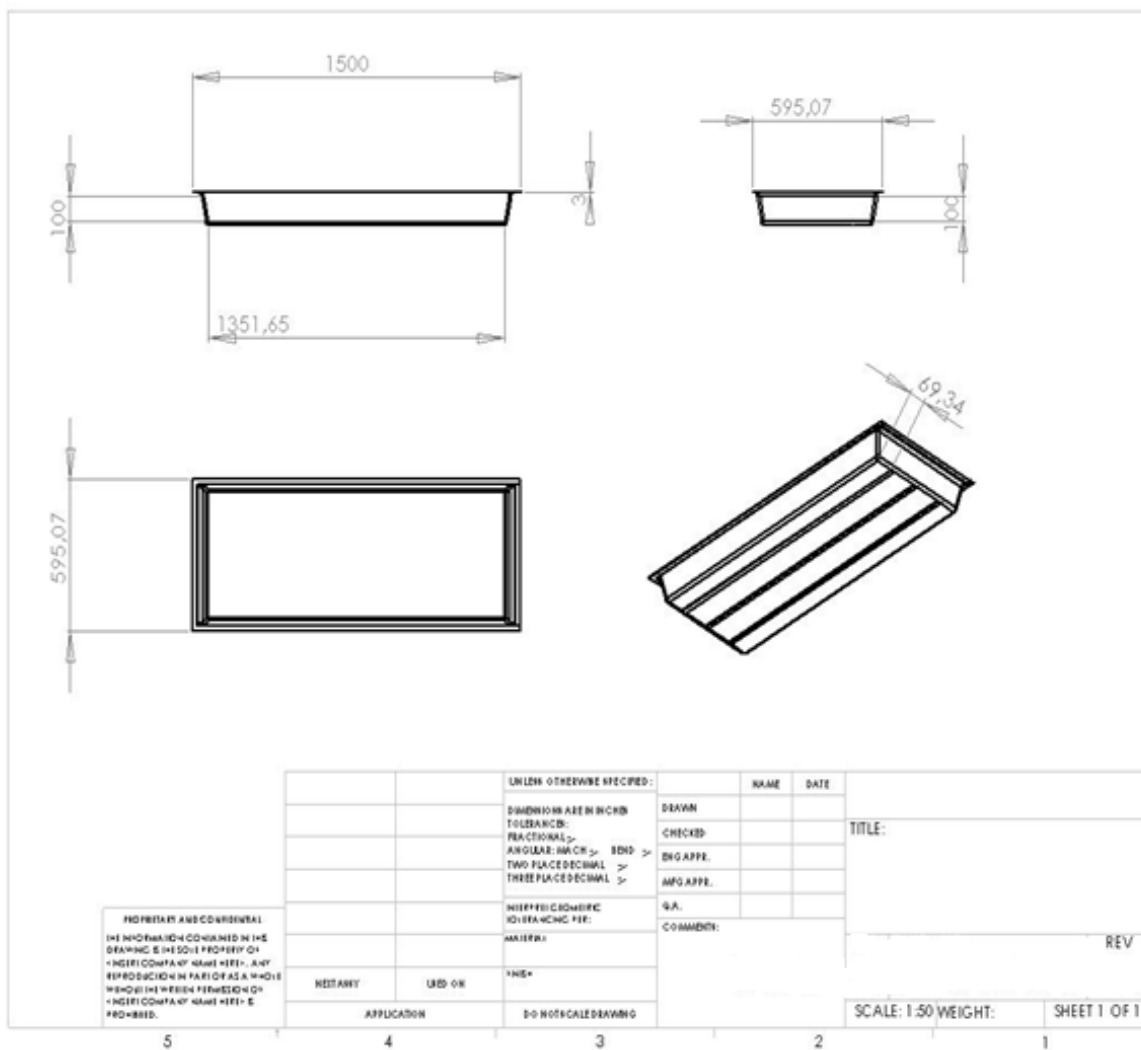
Desenho da peça a ser moldada por RTM *Light*.
